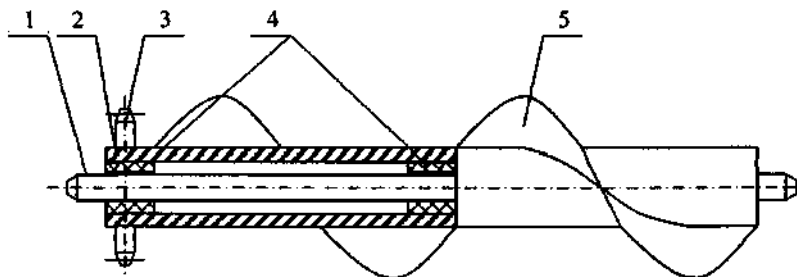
Схема двосекційного розкидального шнека: 1 – вал; 2 – труба; 3 – привідна зірочка; 4 – втулки; 5 – навивка шнека
